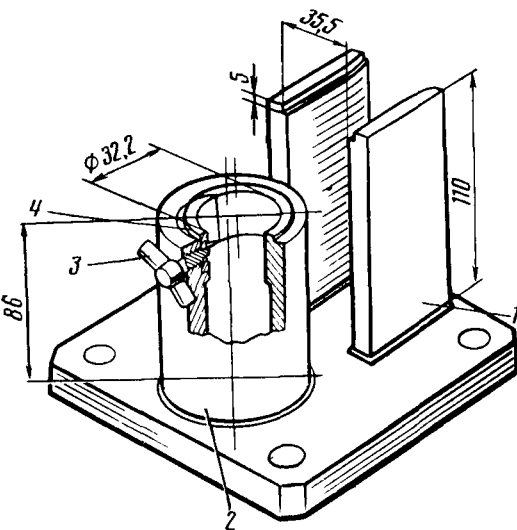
Приспособление для сборки ведомого вала и установки ведущего и ведомого валов:
